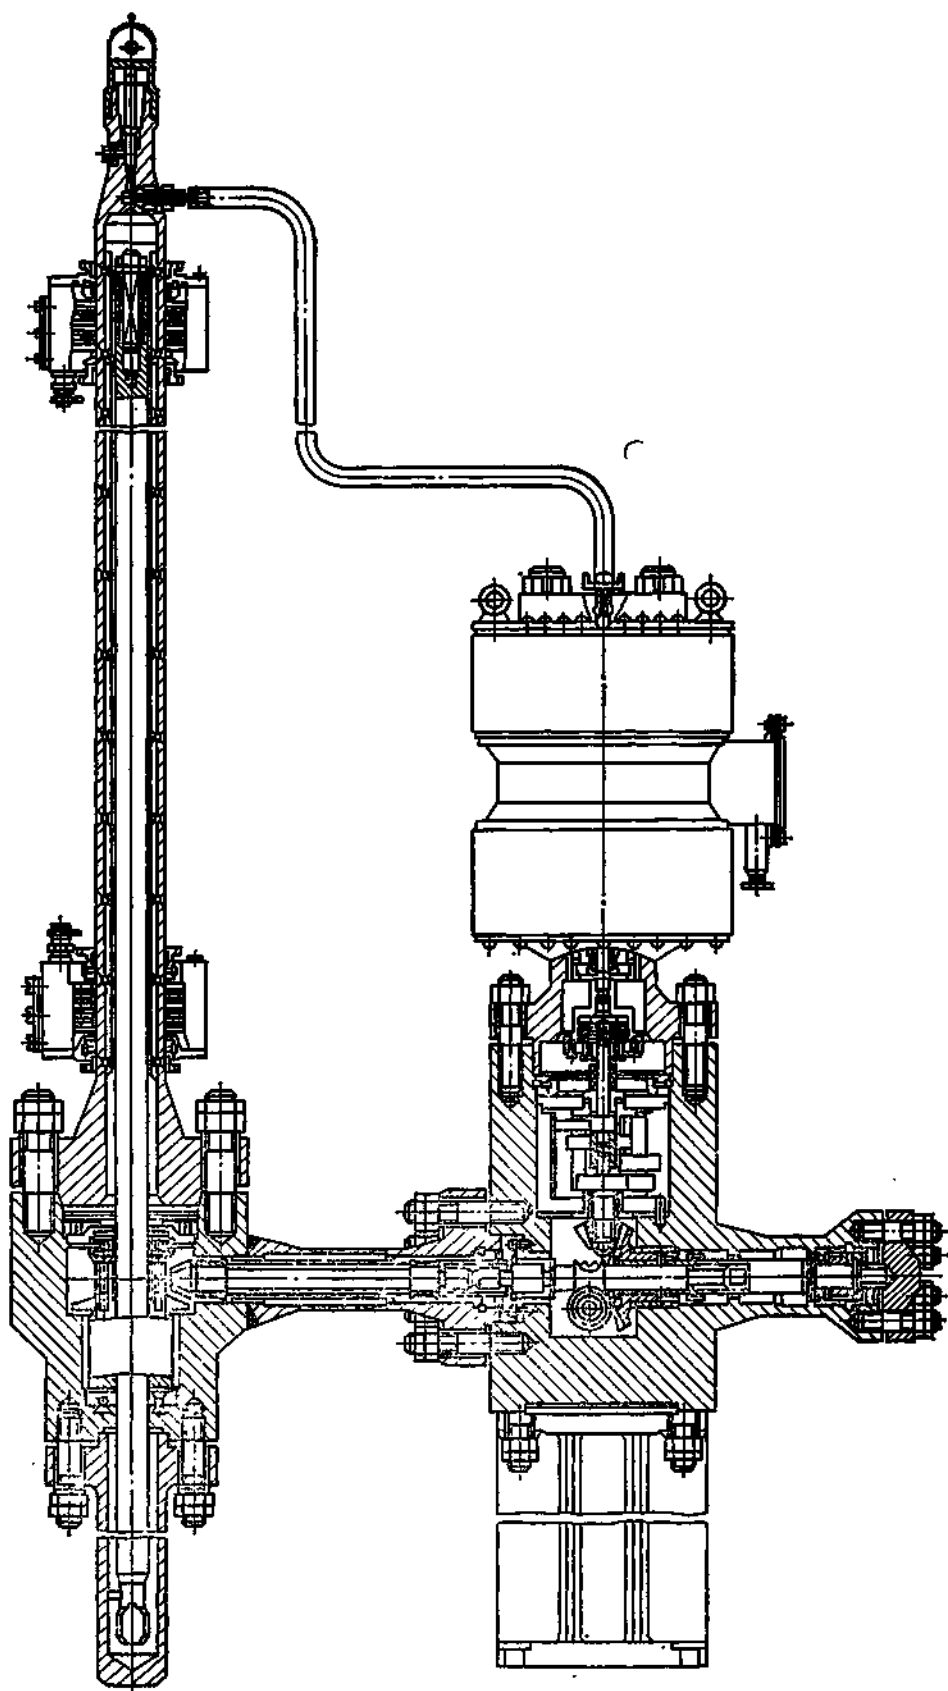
Конструкция исполнительного механизма СУЗ КС
